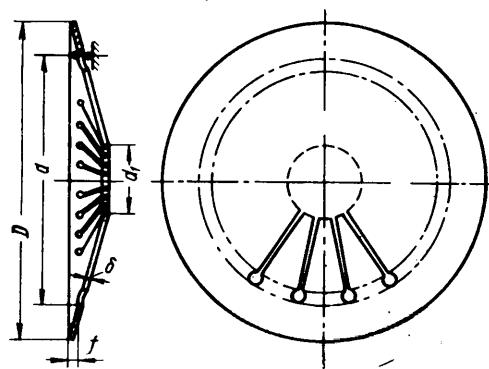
Схема диафрагменной пружины с конструктивными размерами
